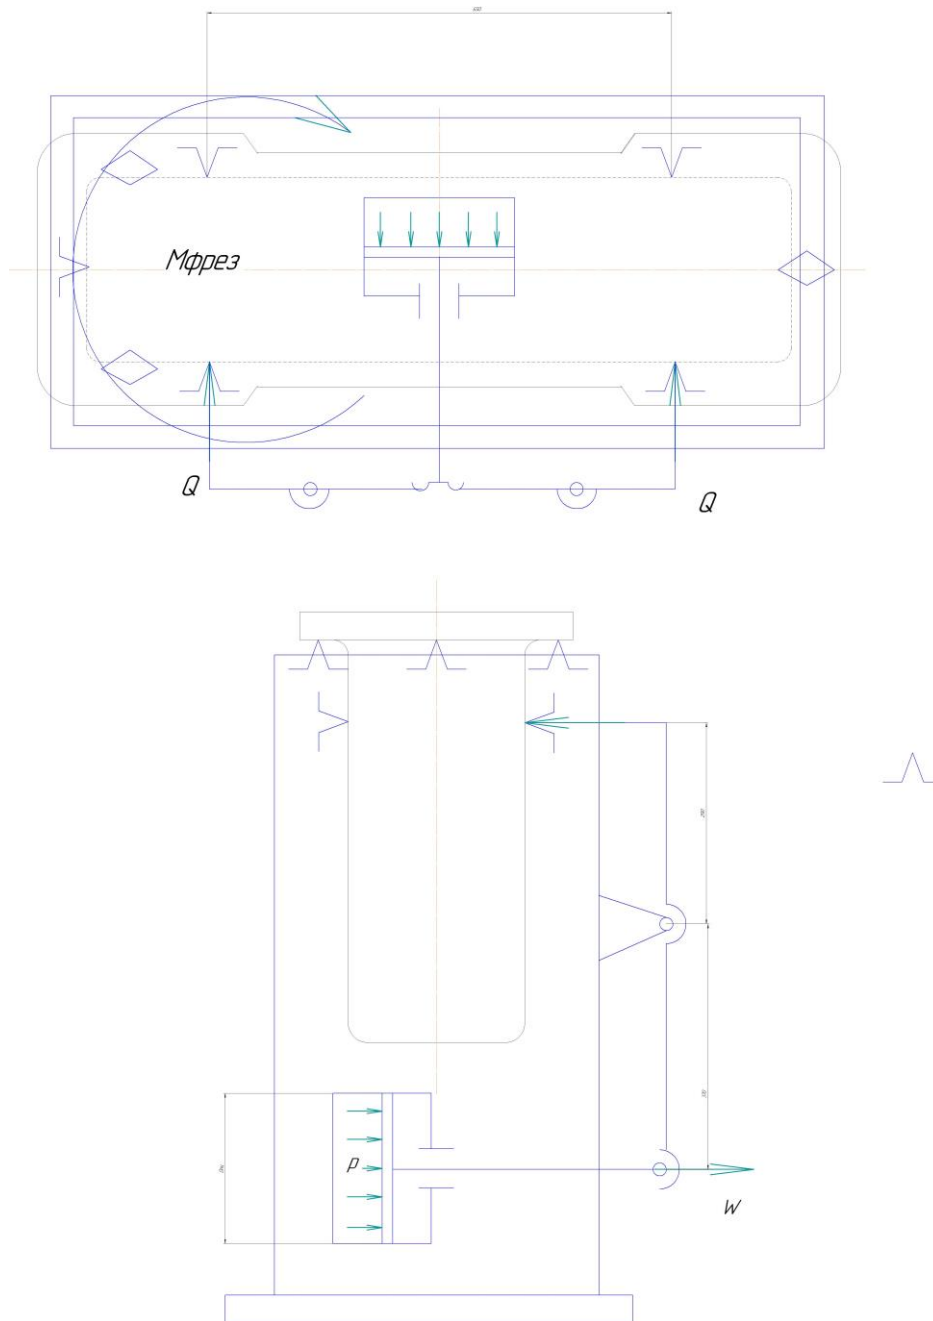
Розрахункова схема фрезерно-свердлильного пристрою
